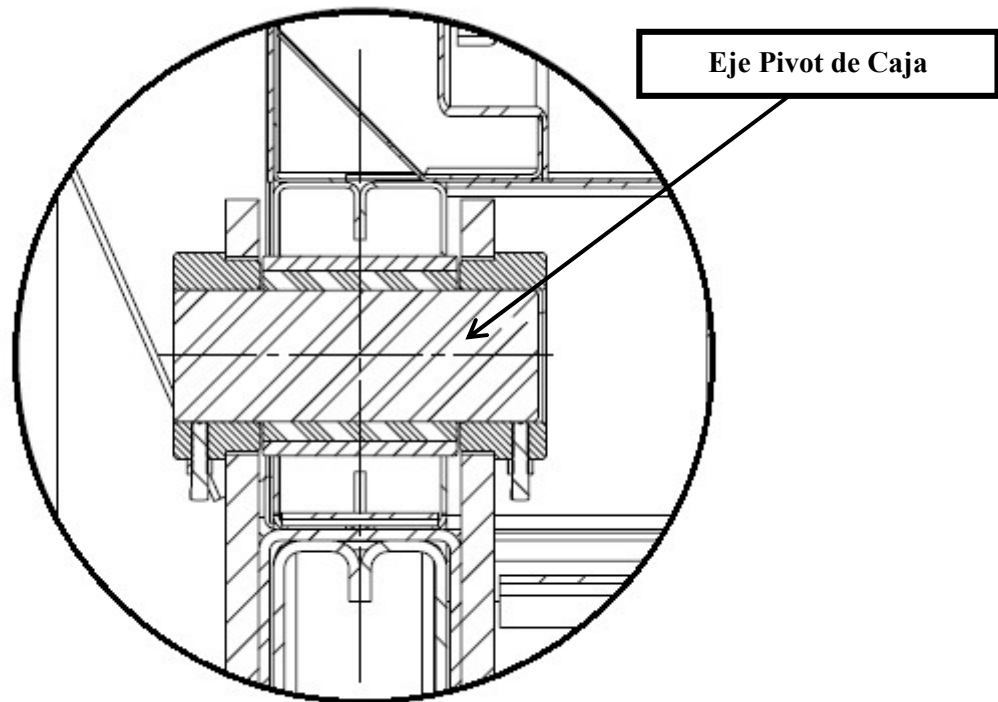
Corte de la estructura chasis y detalle del eje pivot.
